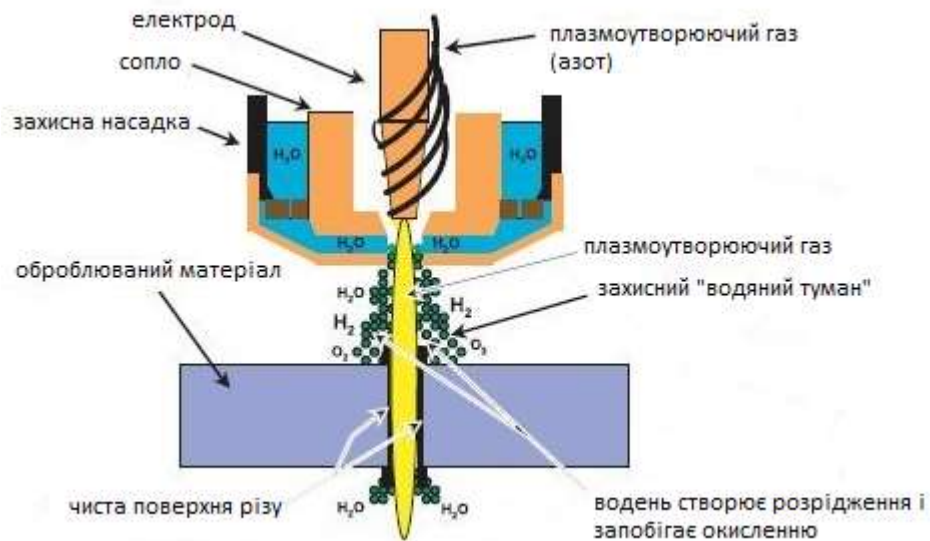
Загальний вигляд установки для плазмового різання та суть процесу
